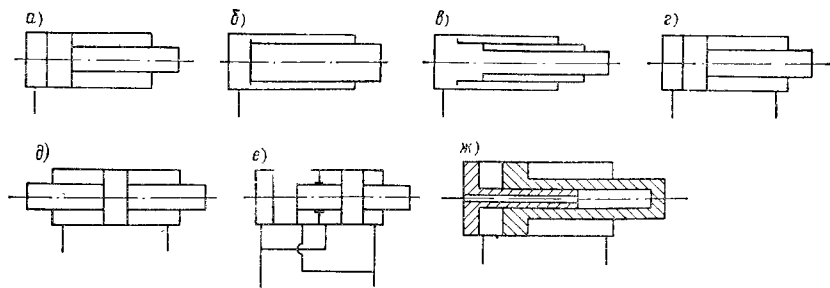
Схемы гидроцилиндров: а — поршневой одностороннего действия; б — плунжерный; в — телескопический; г — поршневой двустороннего действия; д — поршневой двустороннего действия с двусторонним штоком; е — поршневой двухкамерный; ж — ступенчатый
